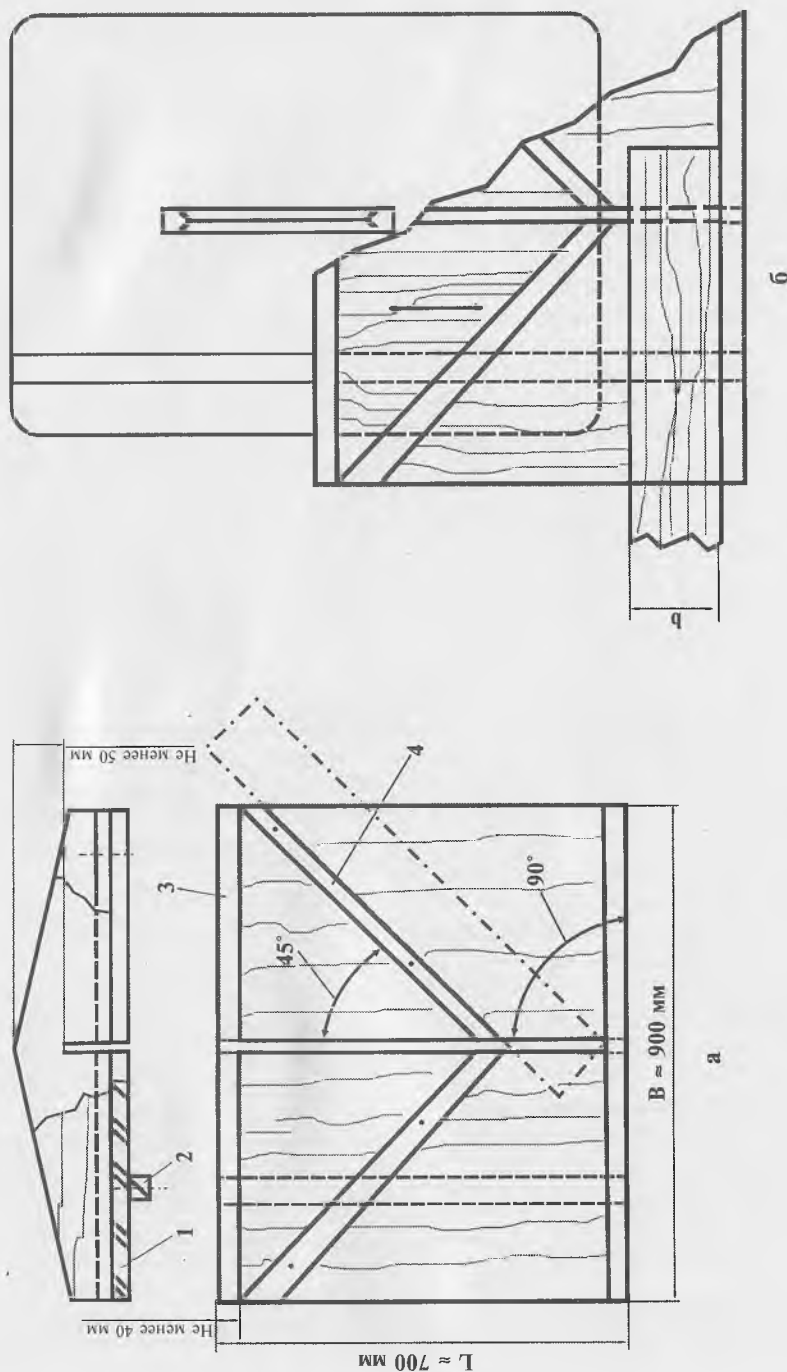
Торцевание заготовок под углами 45° и 90° на круглопилильных станках:
